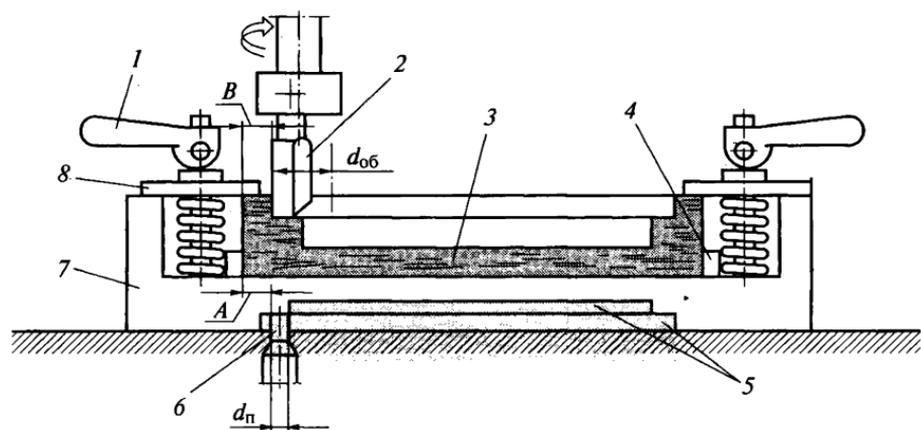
Схема обработки детали в шаблоне на фрезерном станке с верхним расположением шпинделя:
